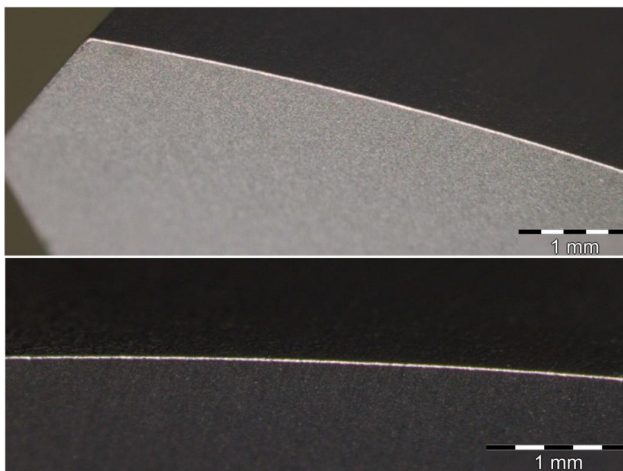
Внешний вид и параметры подготовленной режущей кромки
